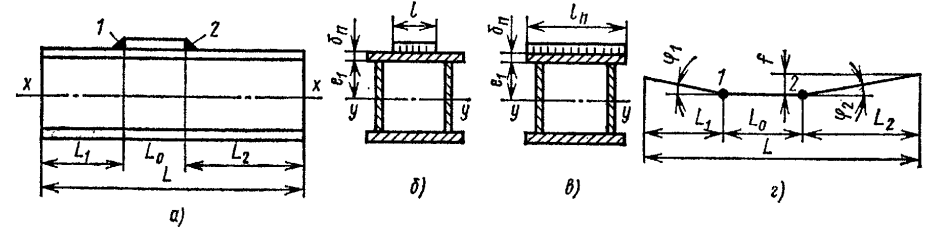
Схемы изгиба балки вследствие поперечной усадки поперечных швов I и 2
